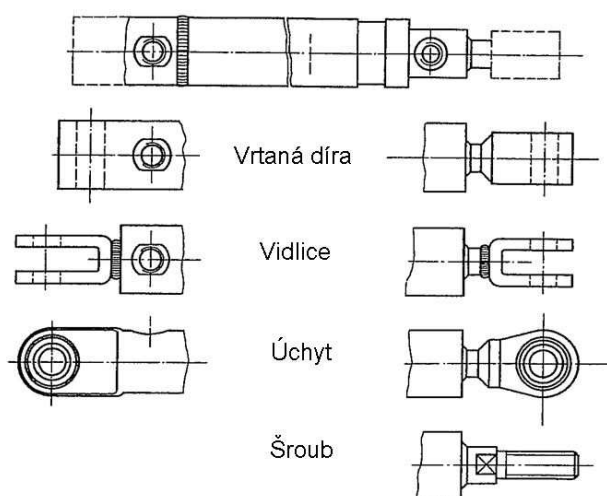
Způsoby upevnění hydromotoru do rámu stroje
